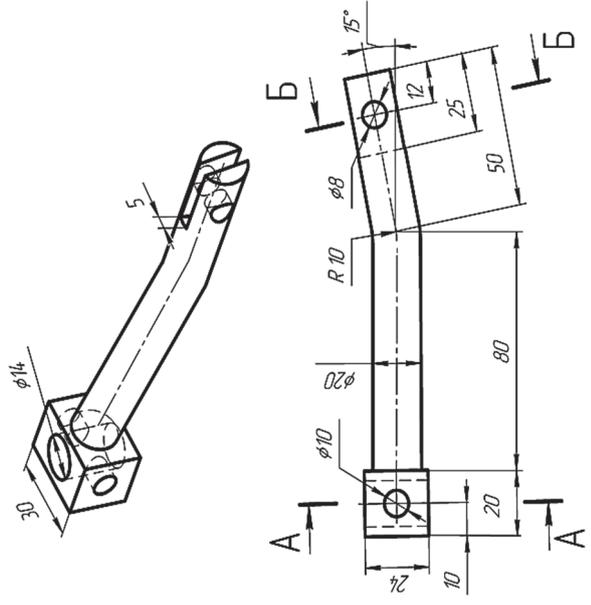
Пример выполнения чертежа детали с целесообразными сечениями
